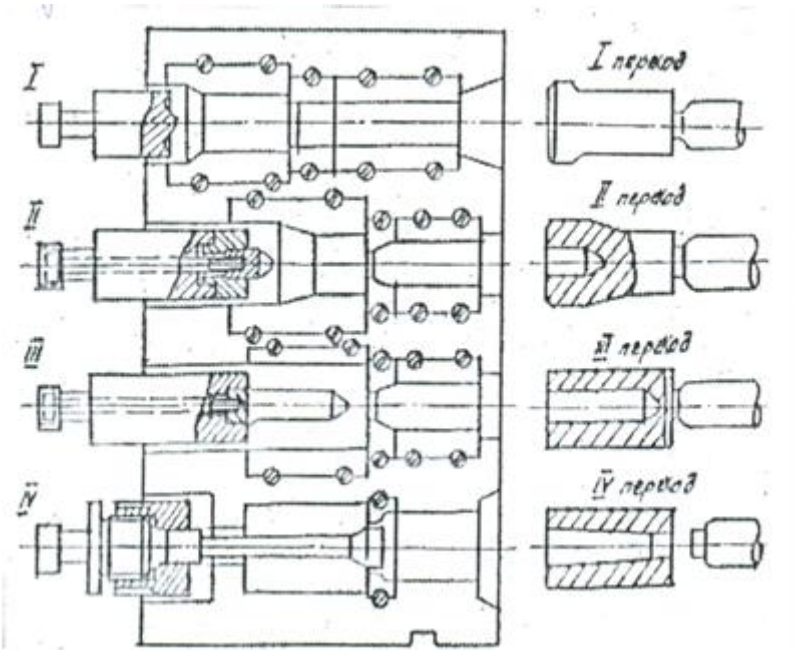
Штампи ГKM для виготовлення поковок типу втулки і переходи штампування
